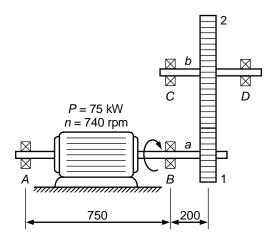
Transmissão por engrenagens cilíndricas de dentes retos.
